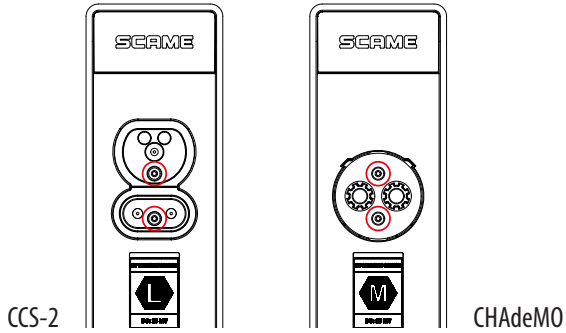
TORNILLOS DE MONTAJE DE LOS SOPORTES FRONTALES
